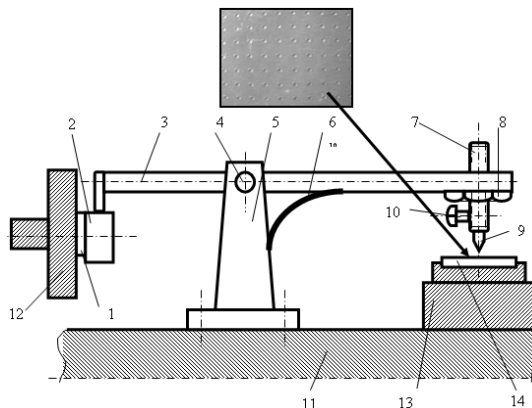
Пристрій для утворення лунок: 1 – приводний вал; 2 – кулачок; 3 – коромисло; 4 – вісь коромисла; 5 – стоек осі коромисла; 6 – пружина; 7 – регулювальний гвинт; 8 – контргайка регулювального гвинта; 9 – бойок; 10 – механізм кріплення бойка; 11 – основа; 12 – патрон; 13 – механізм переміщення; 14 – деталь (зразок)
